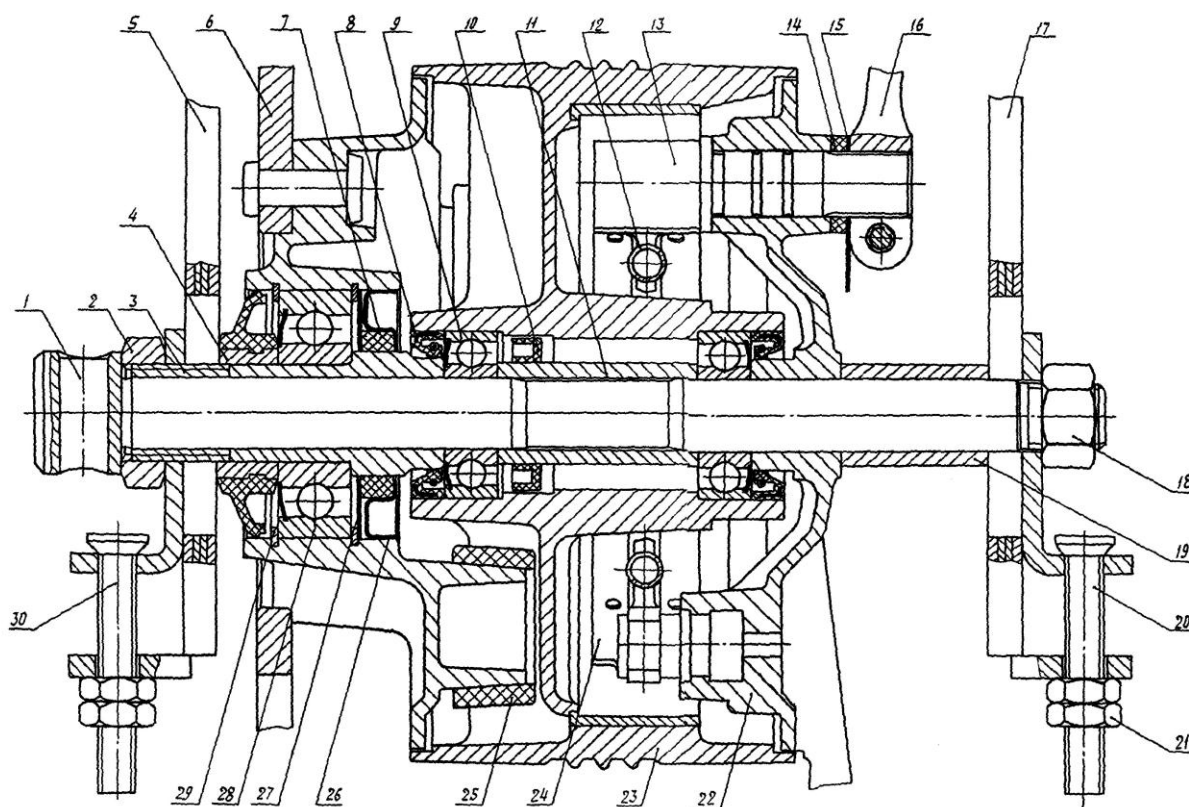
Выпрессовка подшипников и сальников из ступицы колеса
